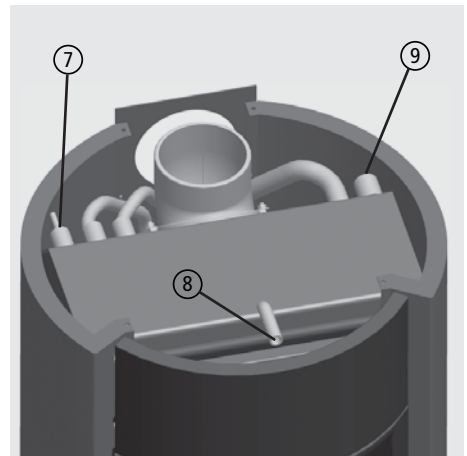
Gewindemuffen für Entlüfter, TAS- und Kesselfühler
